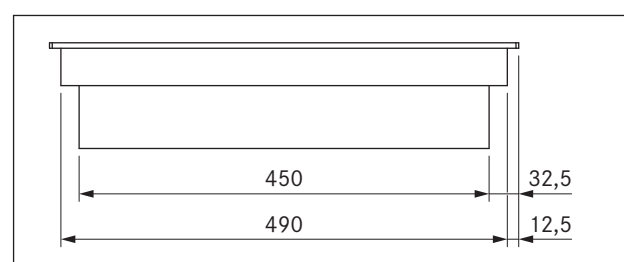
Dimensões do aparelho CKIW, vista lateral
